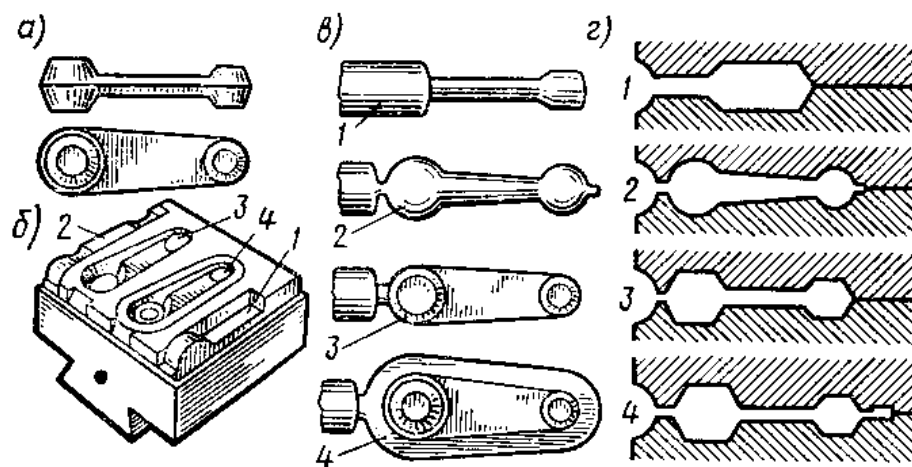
Схема многоручьевого молотового штампа: а – готовая поковка; б – штамп; в – переходы штамповки: 1 – протяжной; 2 – подкатной; 3 – штамповочный в предварительном ручье; 4 – штамповочный в окончательном ручье; г – ручки штампа: 1 – протяжной; 2 – подкатной; 3 – предварительный; 4 – окончательный
